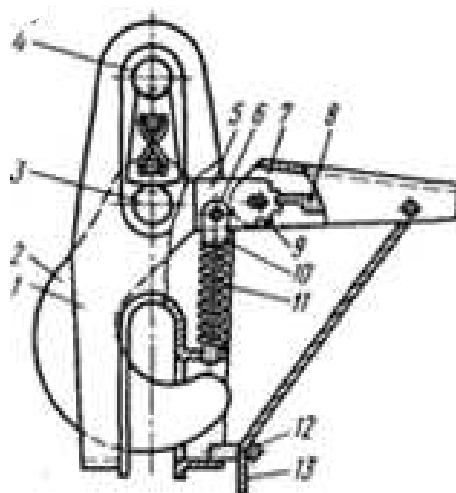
Напівавтоматичний пристрій для дистанційного розстропування:
